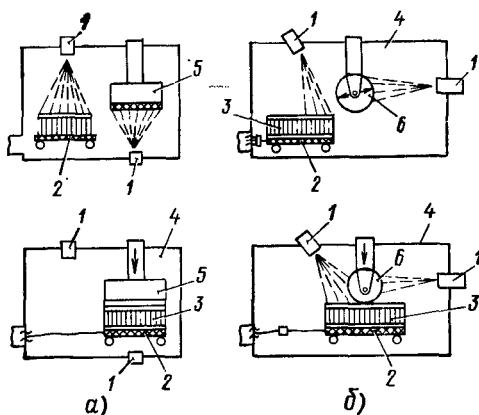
Схема сварки конструкции из титановых сплавов в твердом состоянии с использованием сверхпластичности:
